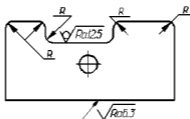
Обозначение шероховатости поверхностей, плавно переходящих одна в другую
